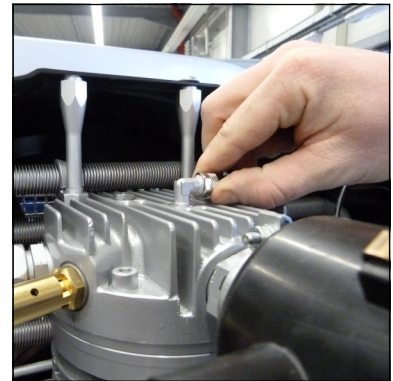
Schlauch für Kurbelgehäuse-entlüftung
